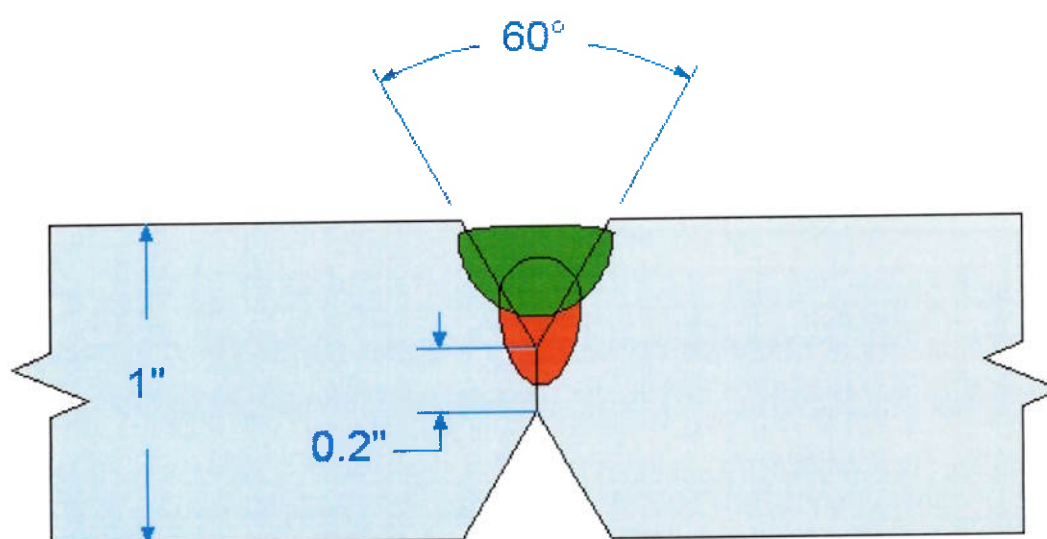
Perfil do cordão de solda do segundo arco. [12]
